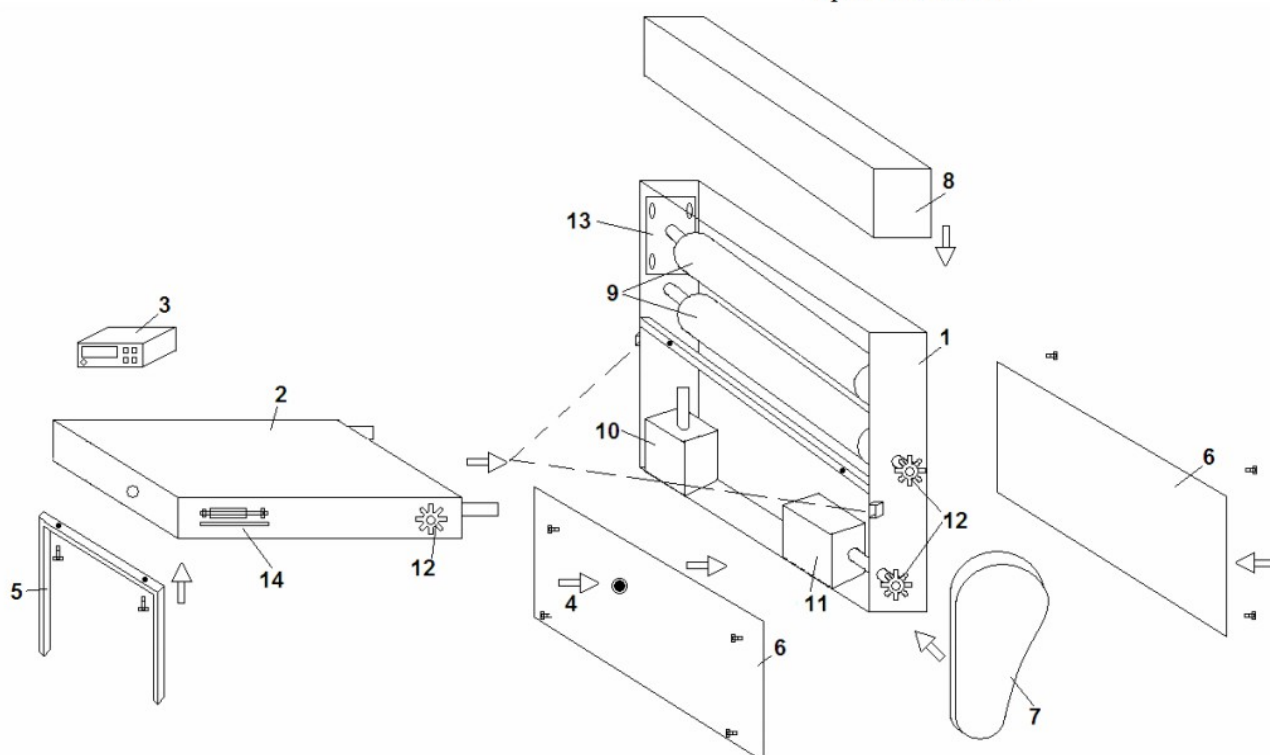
Сборочный чертеж установки АИДК-20Ц
